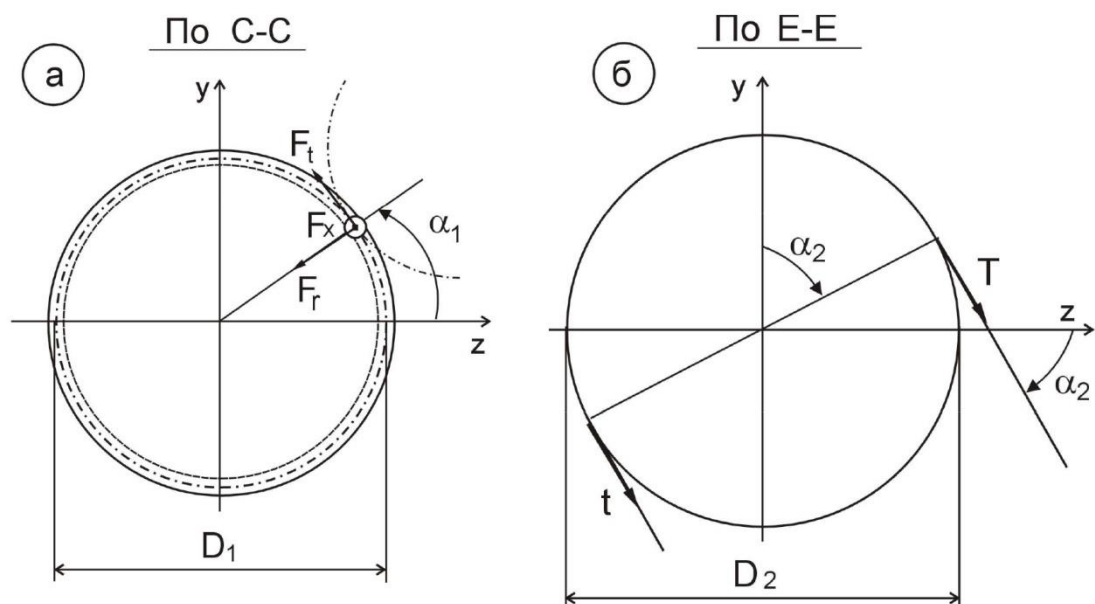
Сечения косозубого зубчатого колеса (а) и ведущего шкива (б).
